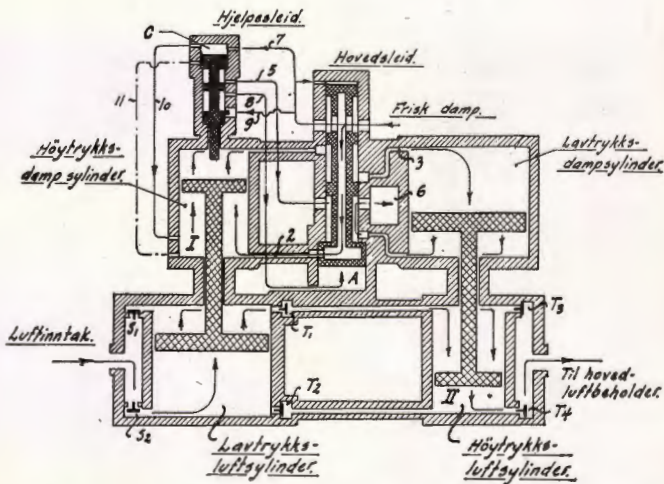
P-styring for dobbelt komponent luftpumpe.
